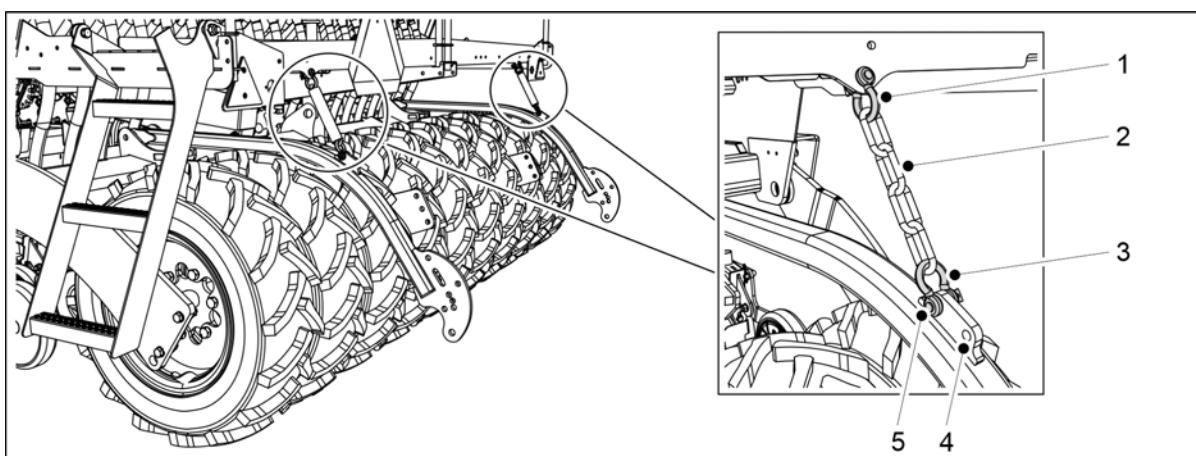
82. Montáž rameň zadních bran
